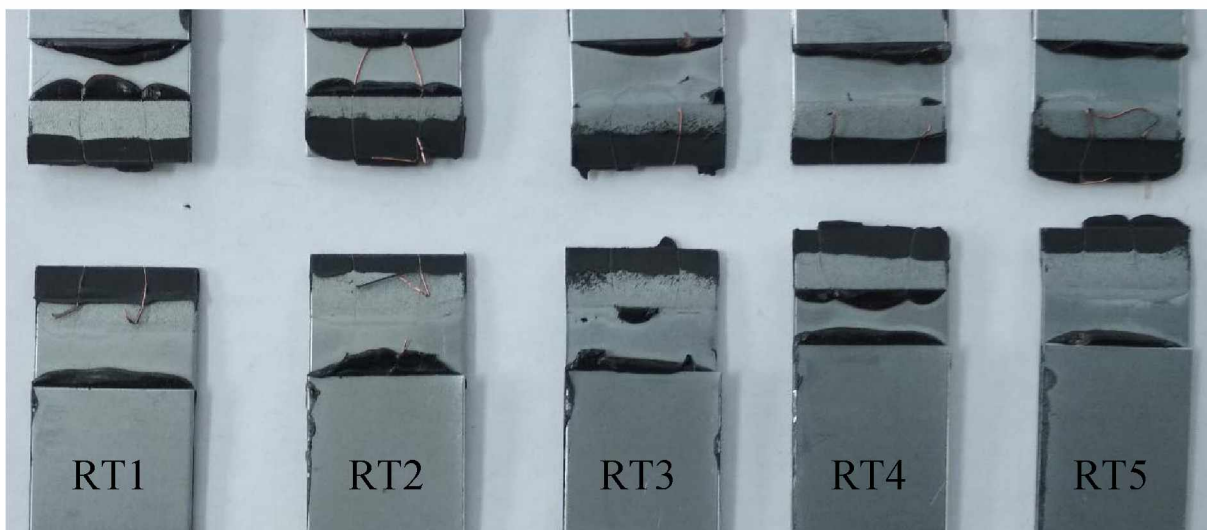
Tvar vzorku pro testování dynamické testování bez zpevnění
